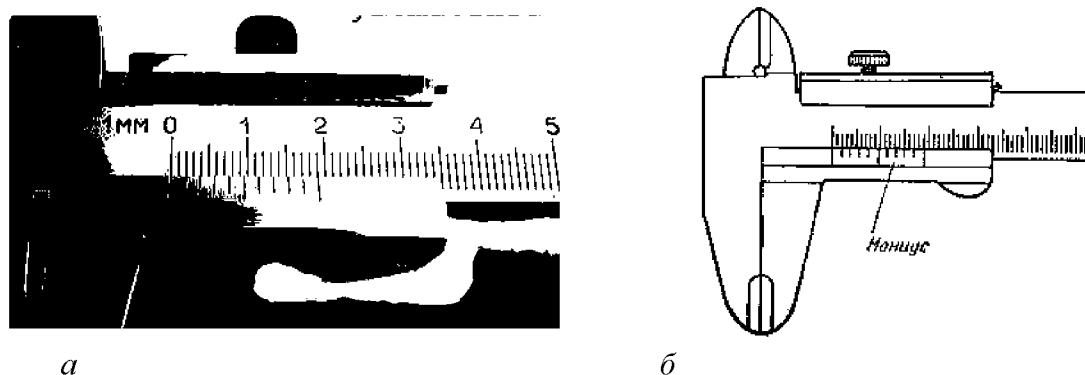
Устройство нониуса штангенинструмента: *а* – общий вид; *б* – схема
